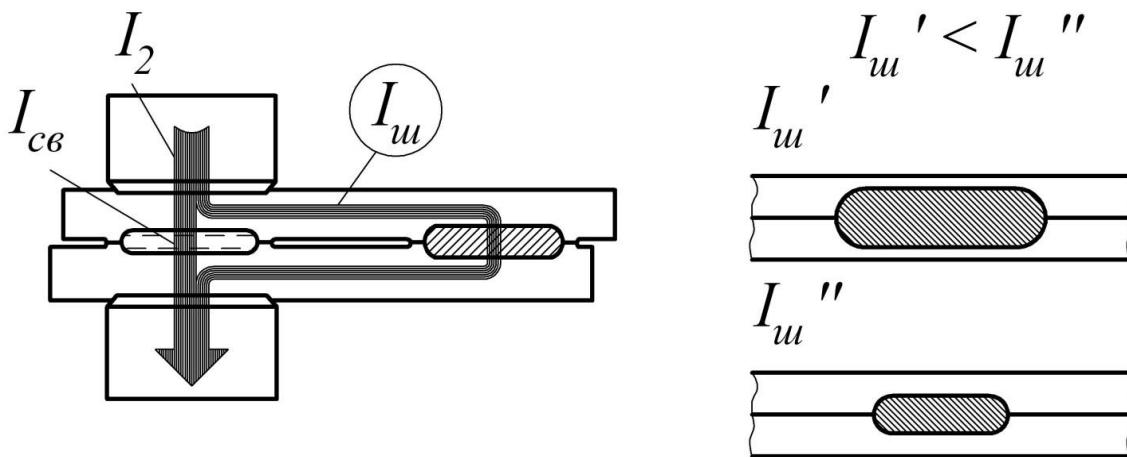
Шунтирование сварочного тока при контактной сварке
